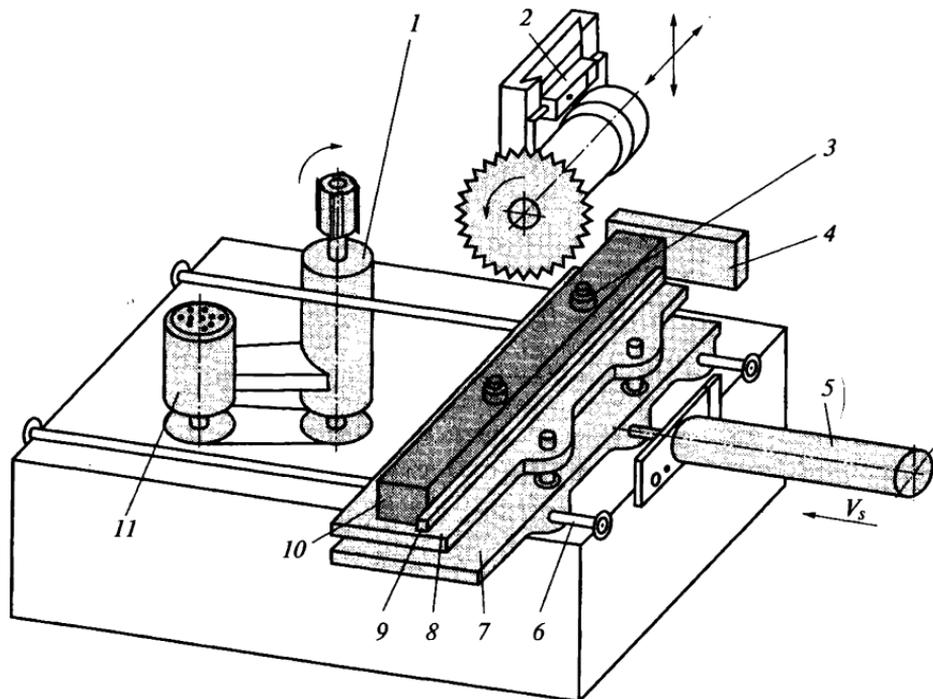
Шипорезный станок для выработки клиновых шипов:
